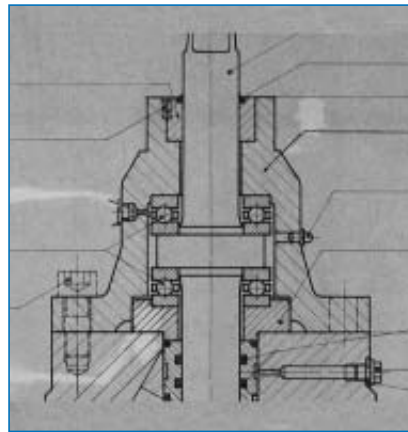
Ausschnitt einer Transparentzeichnung bezüglich der Konstruktion eines Schiebers des Typs VAG ELITA, Baujahr 1972
